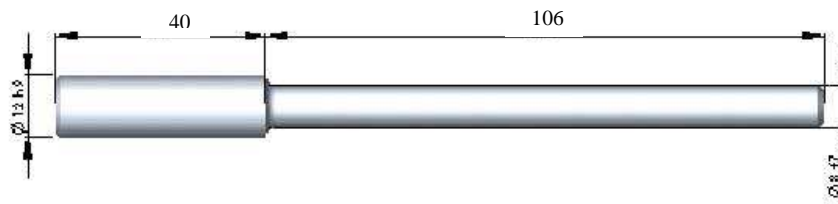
Géométrie de l'éprouvette usinée pour les tests de fatigue.
